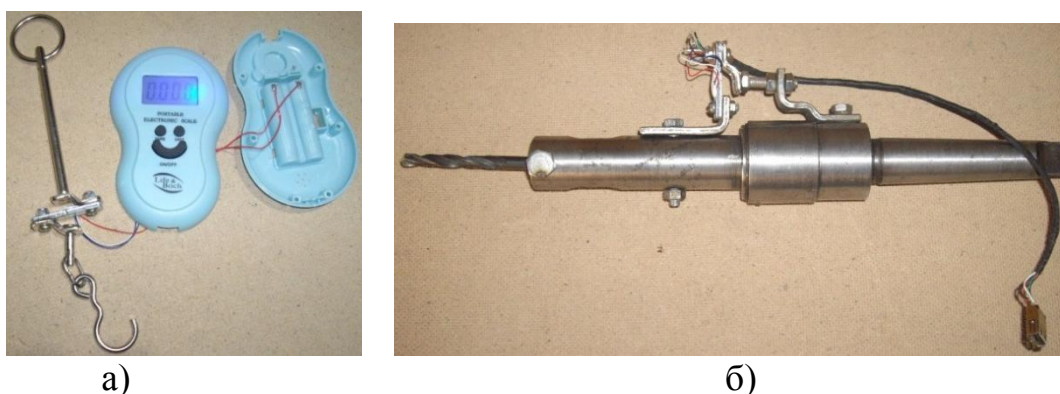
Пристрій для вимірювання осьового зусилля при свердлінні:
